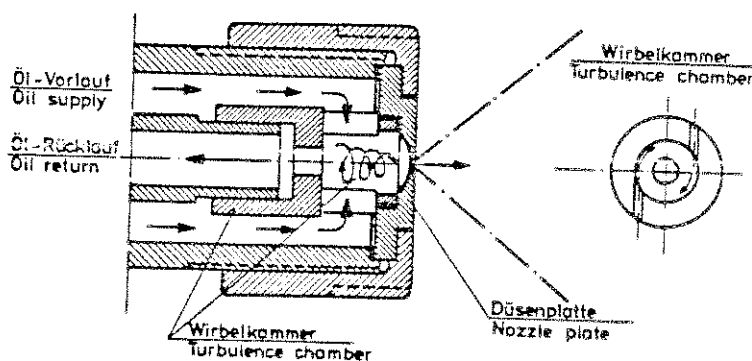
Öl-Rücklaufbrenner für Heizöl
